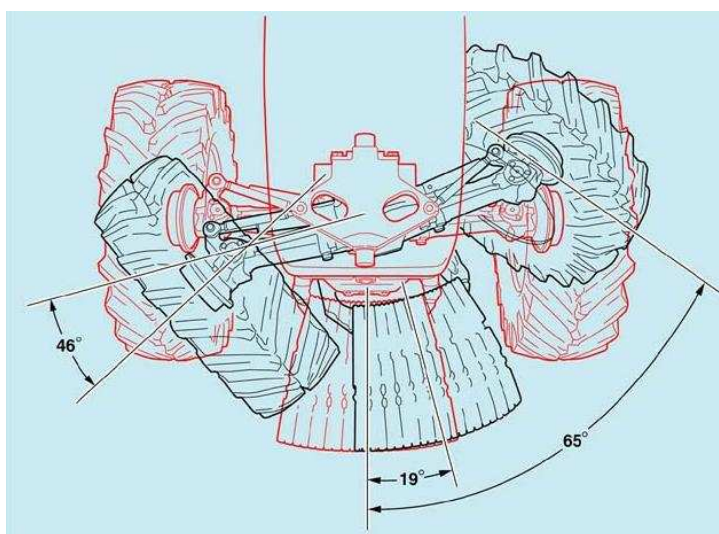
Nezávisle odpružená přední hnací náprava Carraro [18]
